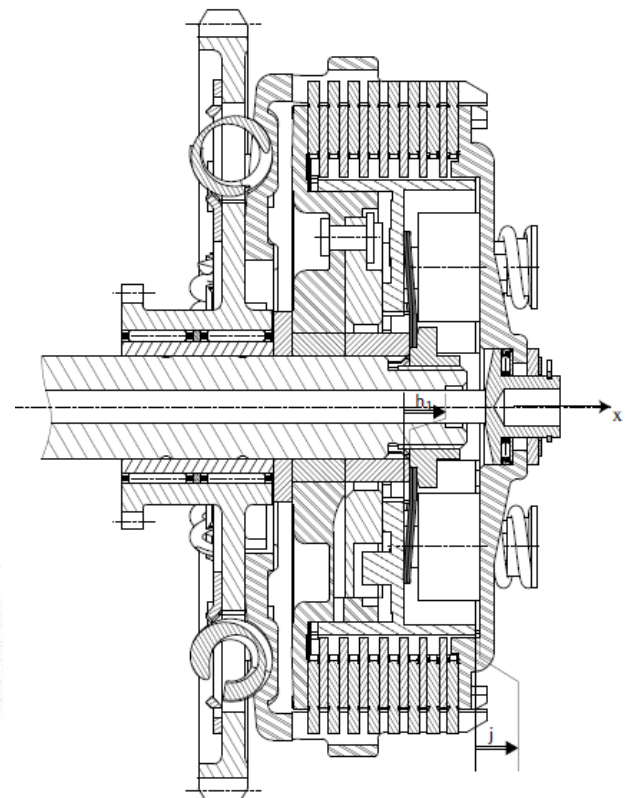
Vue d'ensemble de l'embrayage « sliding-clutch »
